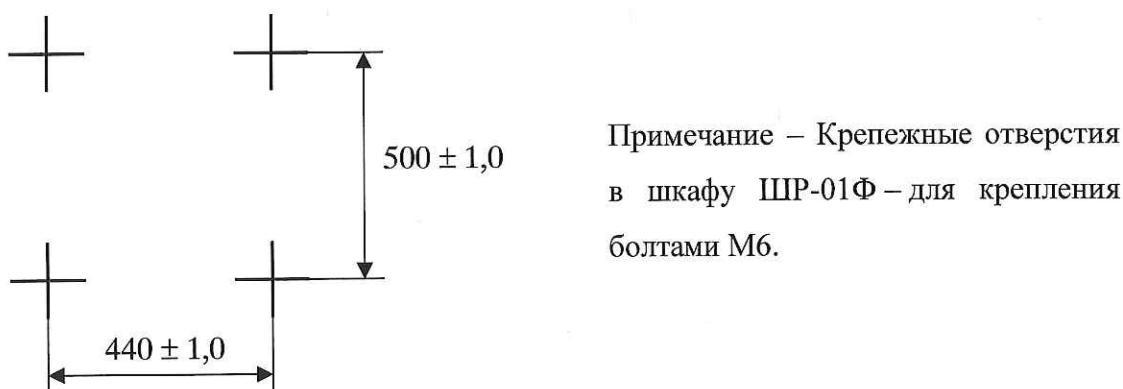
Разметка для крепления шкафа ШР-01Ф
